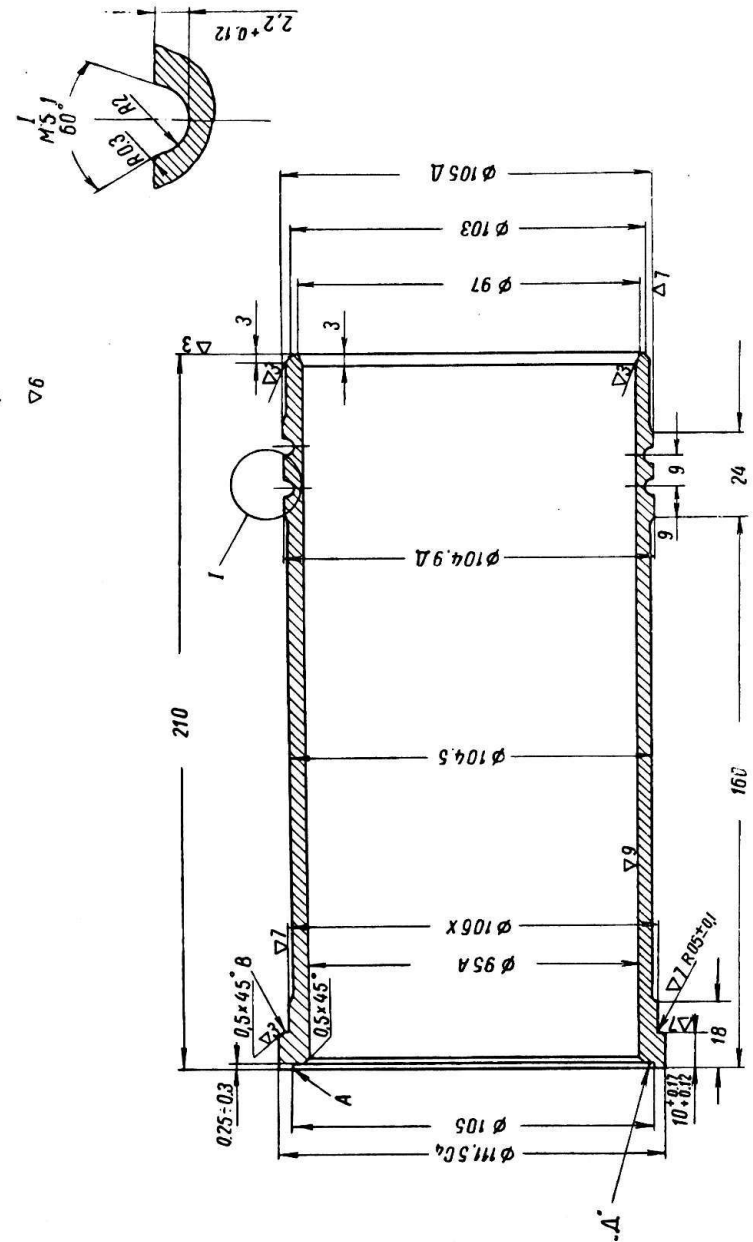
Втулка цилиндра — 7Д6-13.00.03
